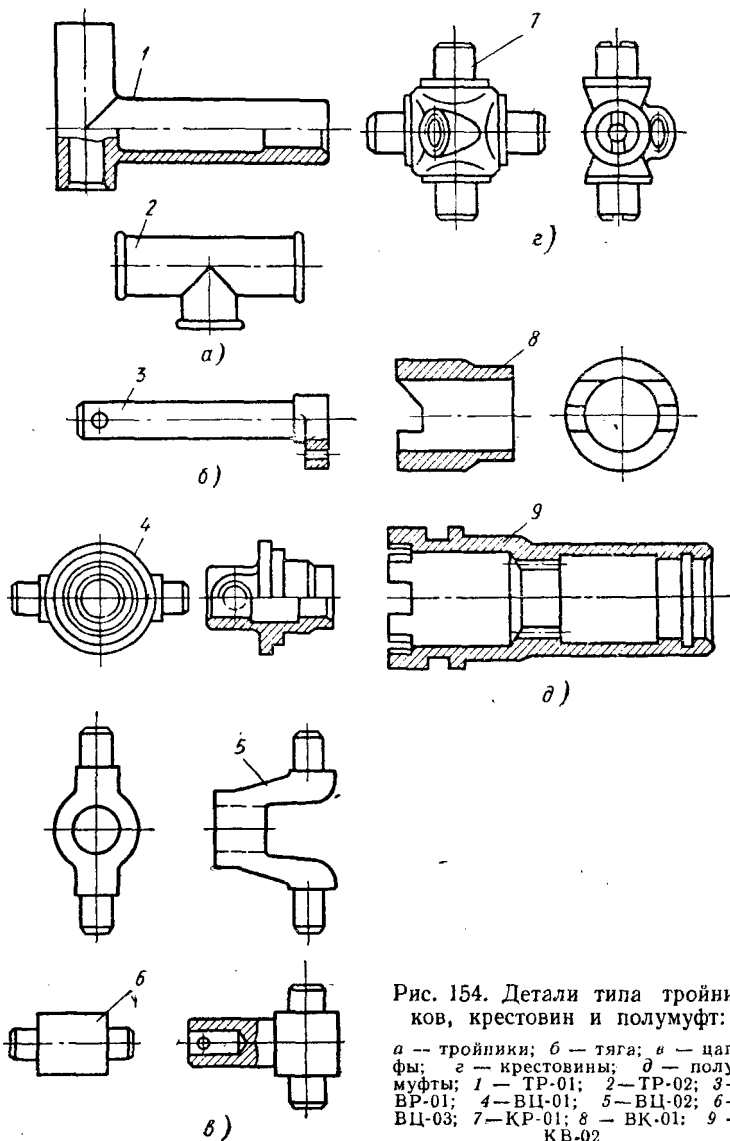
Детали типа тройников, крестовин и полумуфт:
